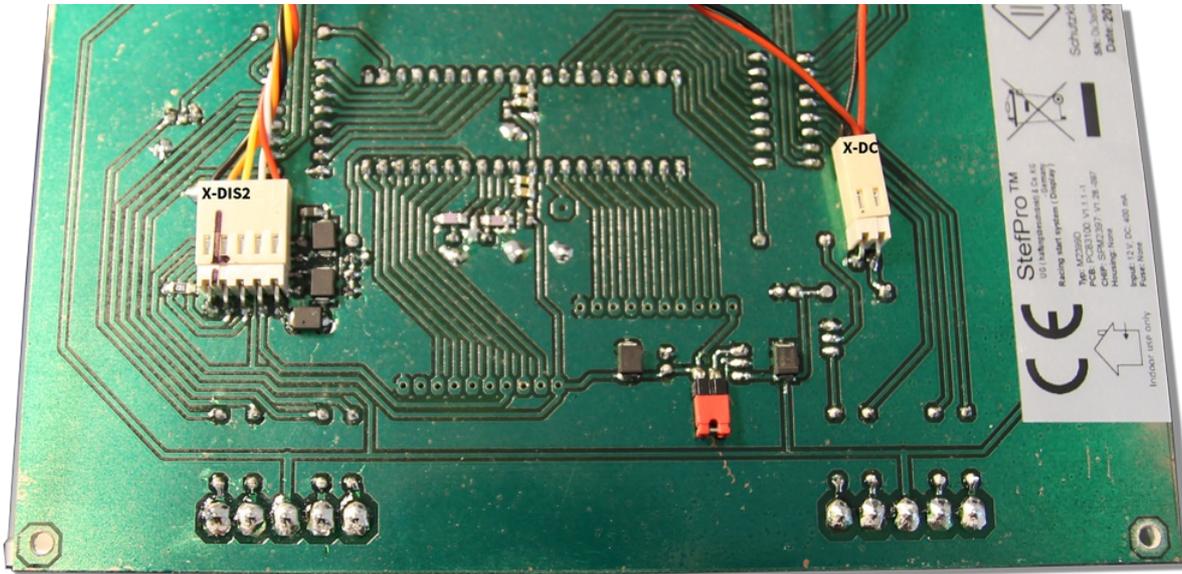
Stecker Beschreibung zum Modul PCB3100
